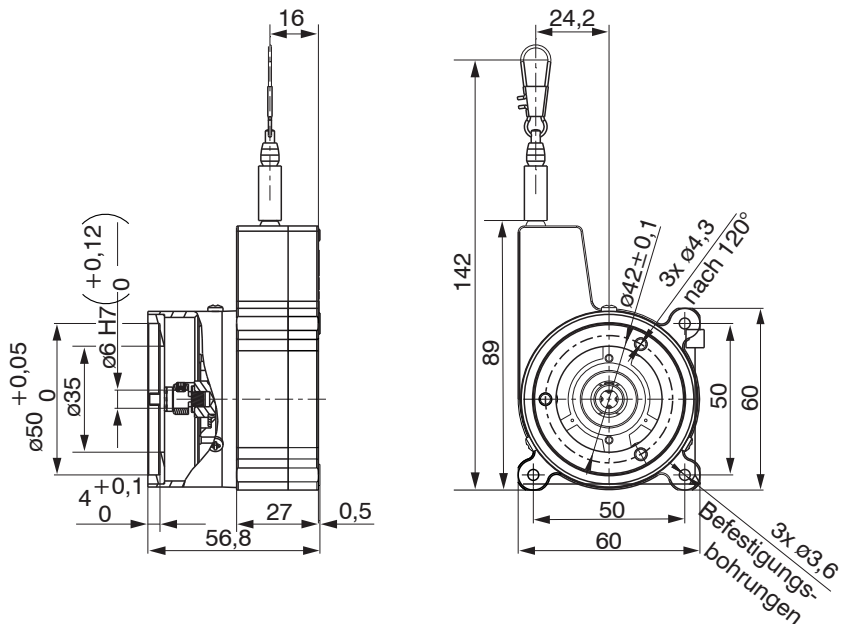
Maßzeichnung WPS-2400-MK60-M, Abmessungen in mm
